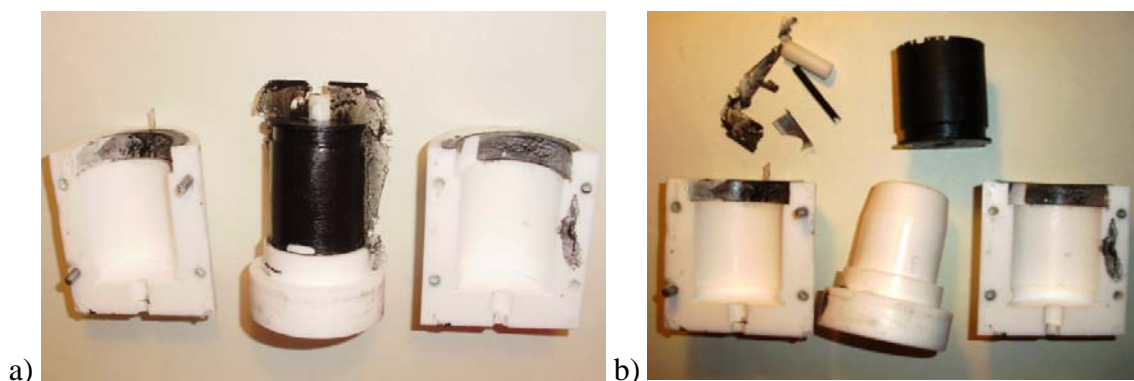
a) Nedotečený prototyp b) Rozlámáný prototyp
